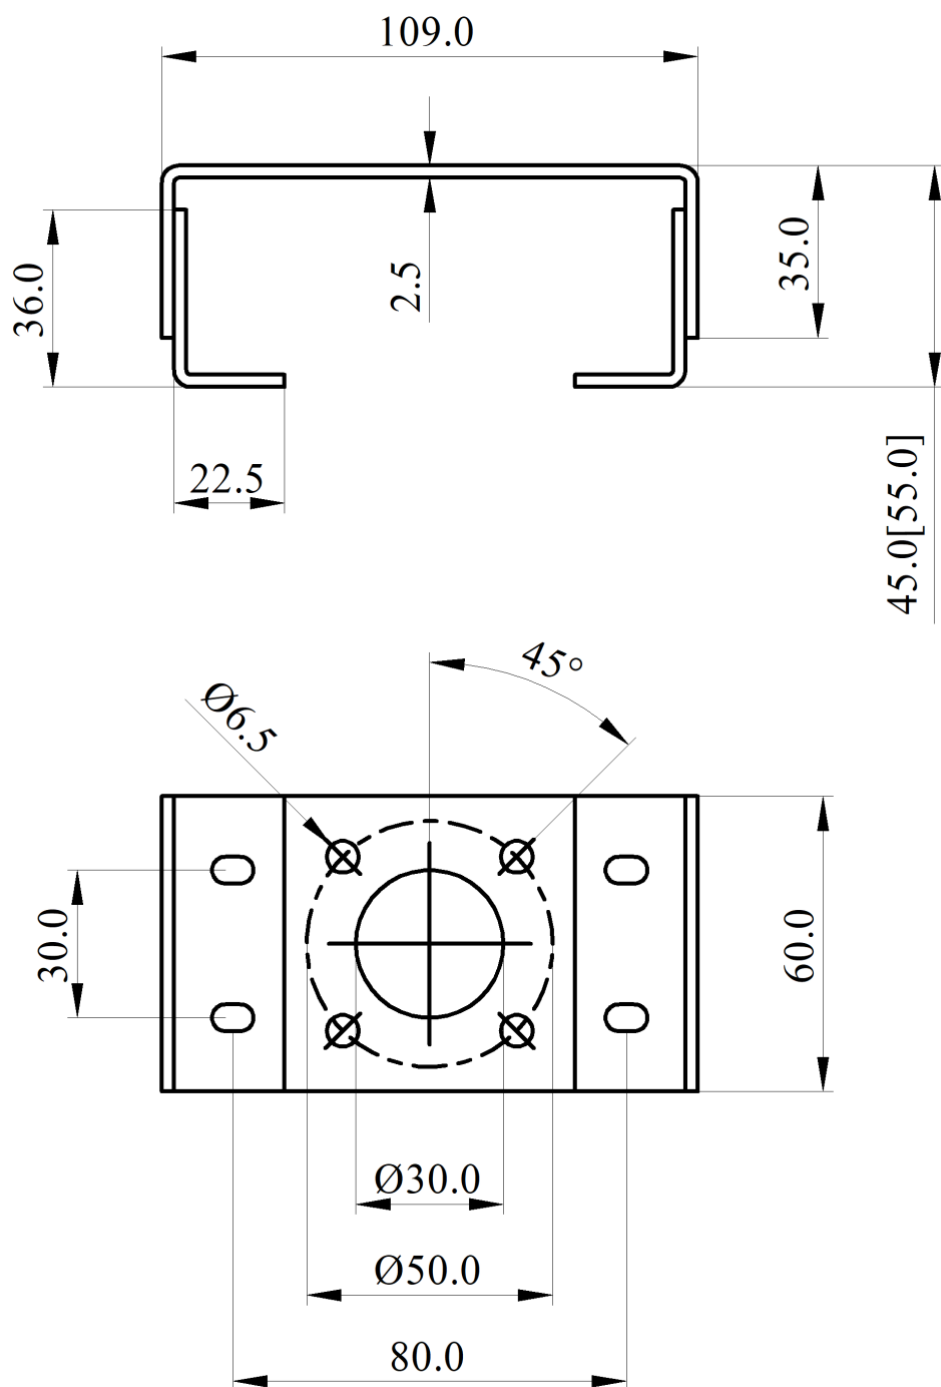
Монтажный кронштейн с угловым ходом, тип А
